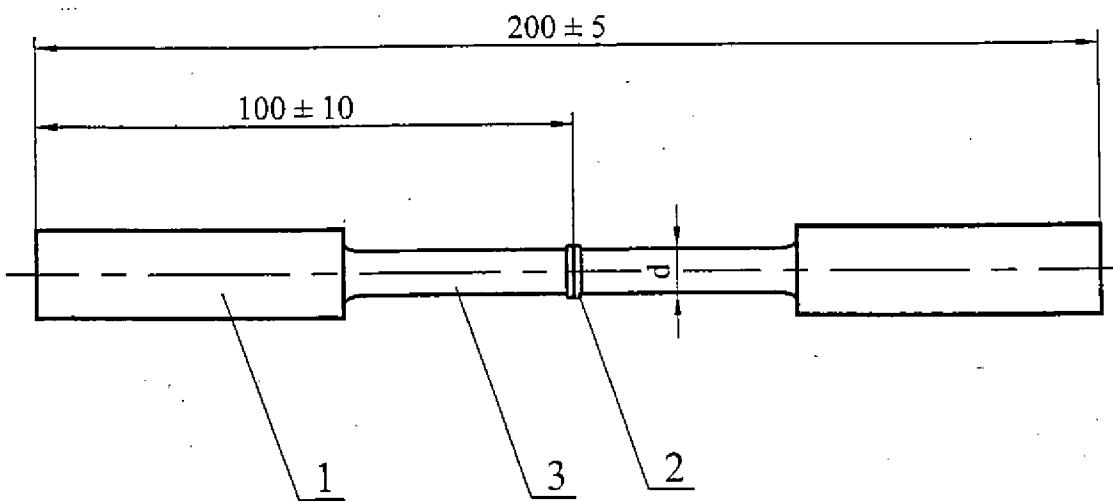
Соединитель рельсовых стыковой приварной СРФ
